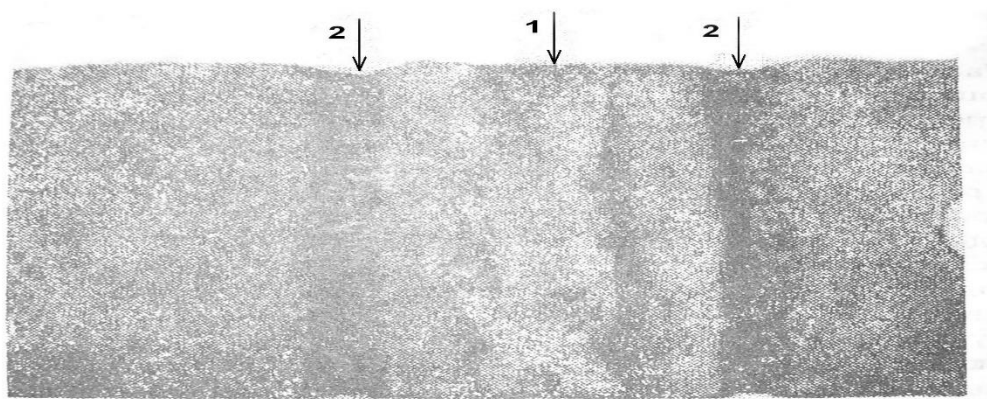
Коррозионное разрушение стальной конструкции в области сварного шва: 1 – сварной шов; 2 – коррозионное разрушение в околошовной зоне
